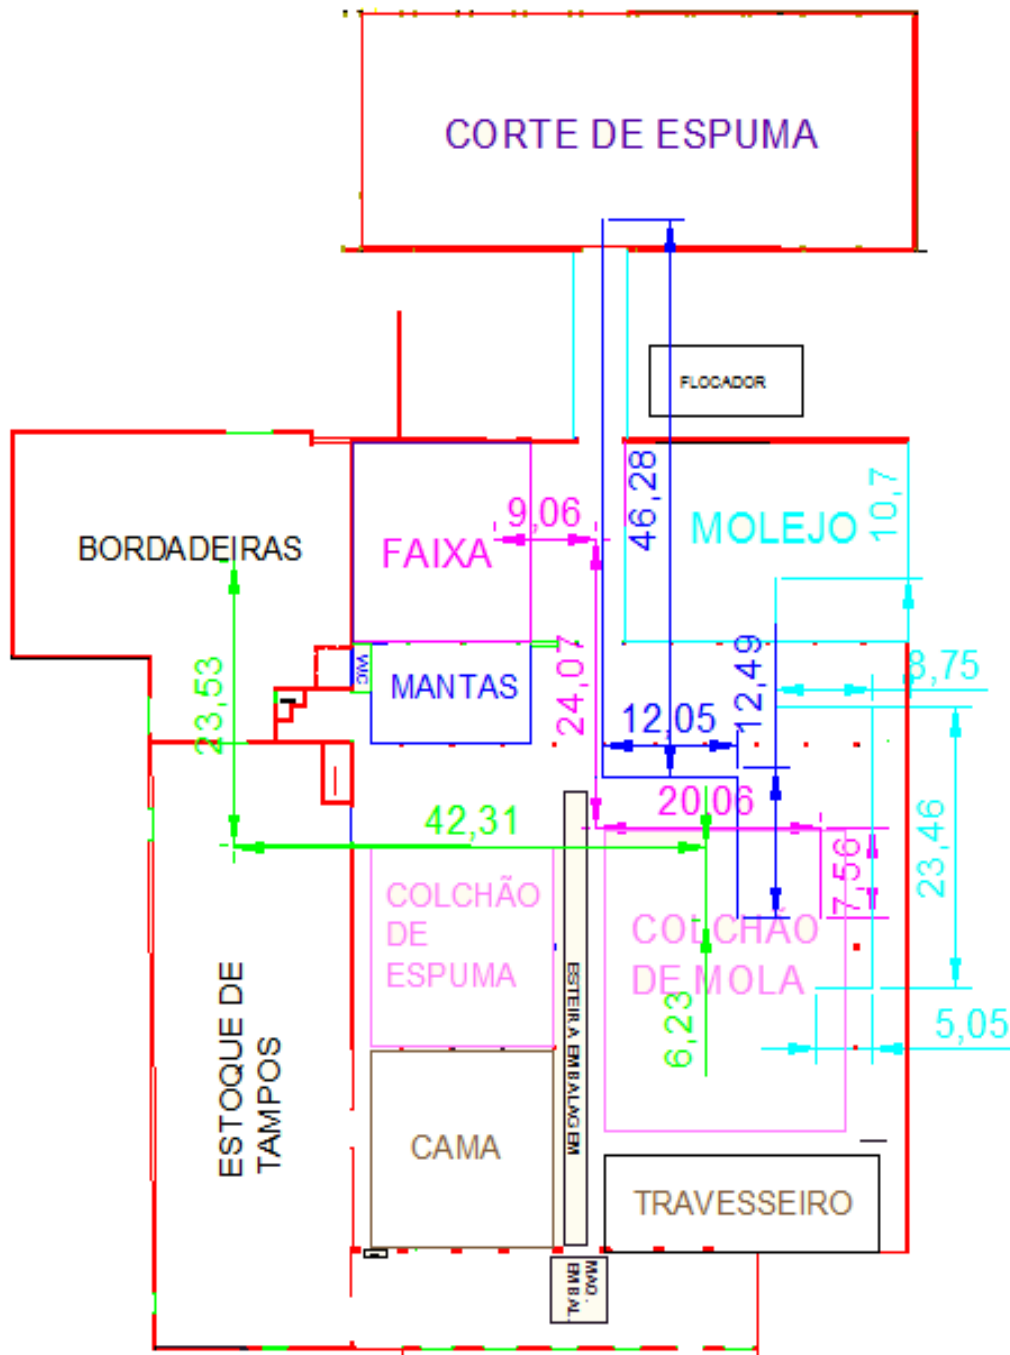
Proposta Planta Baixa Distancias percorridas proposta
